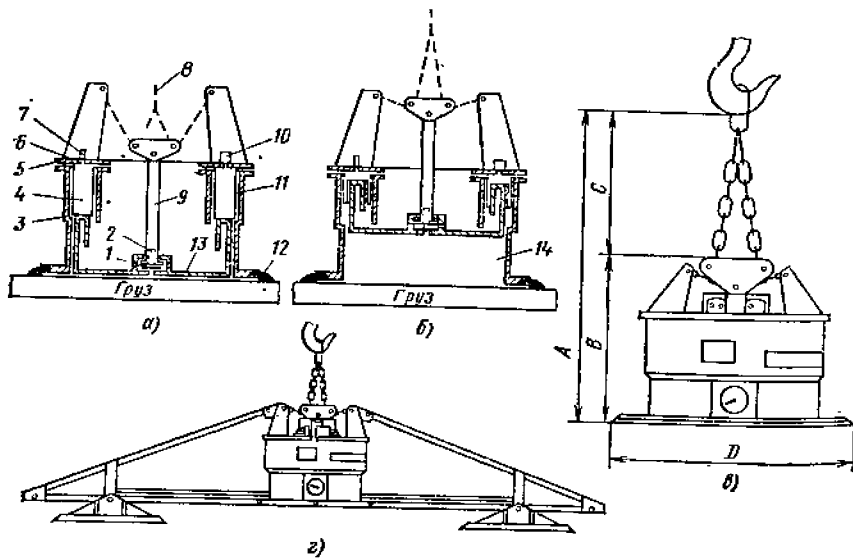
Вакуумное ГУ фирмы Ваку-лифт: а — схема ГУ при нижнем положении поршня; б — то же, в процессе подъема груза; в — общий вид ГУ с габаритными размерами; г — ГУ с несколькими вакуумными захватными камерами на траверсе
